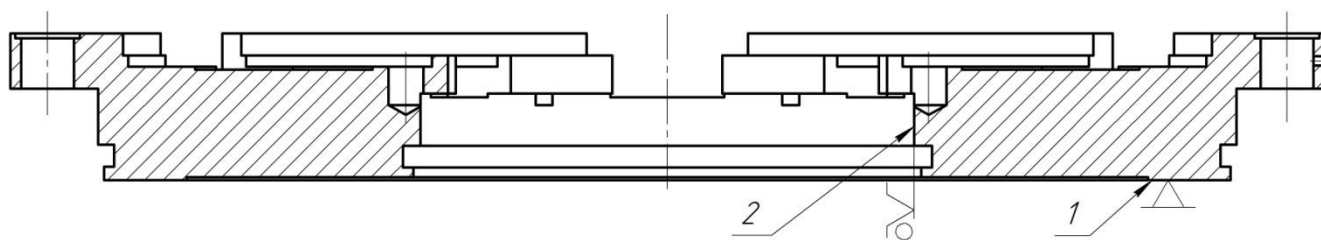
Схема базування деталі при контролі торцевого биття
